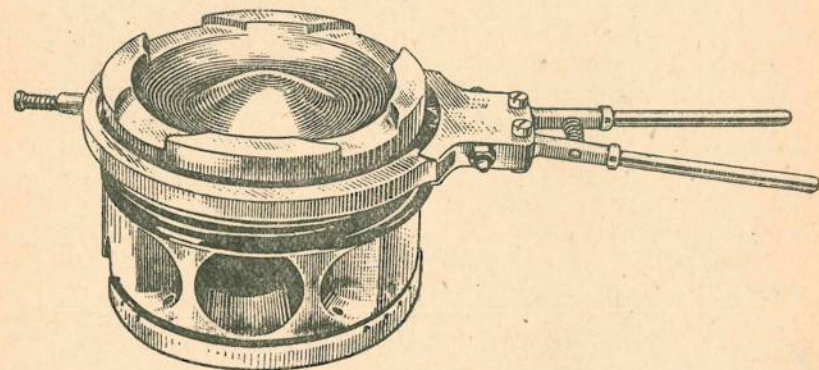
Снятие поршневых колец с поршня при помощи приспособления
